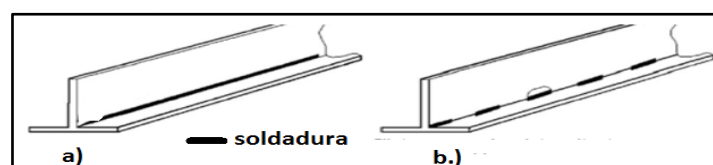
Tipo de soldadura longitudinal; a) continua, b) intermitente.
